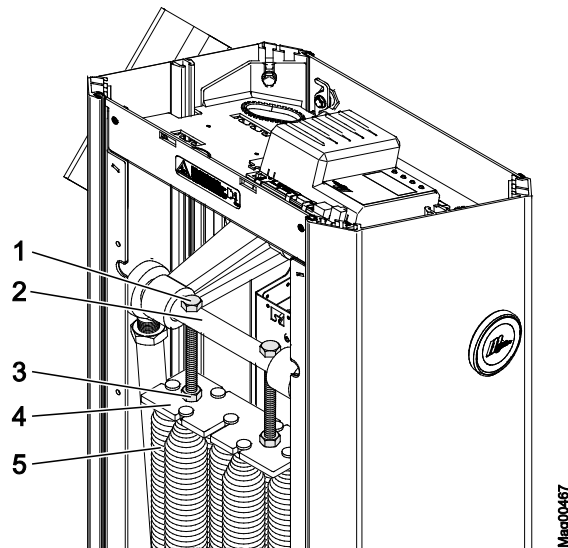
Ausgleichsfedern Access XL2 und Access XXL einstellen
